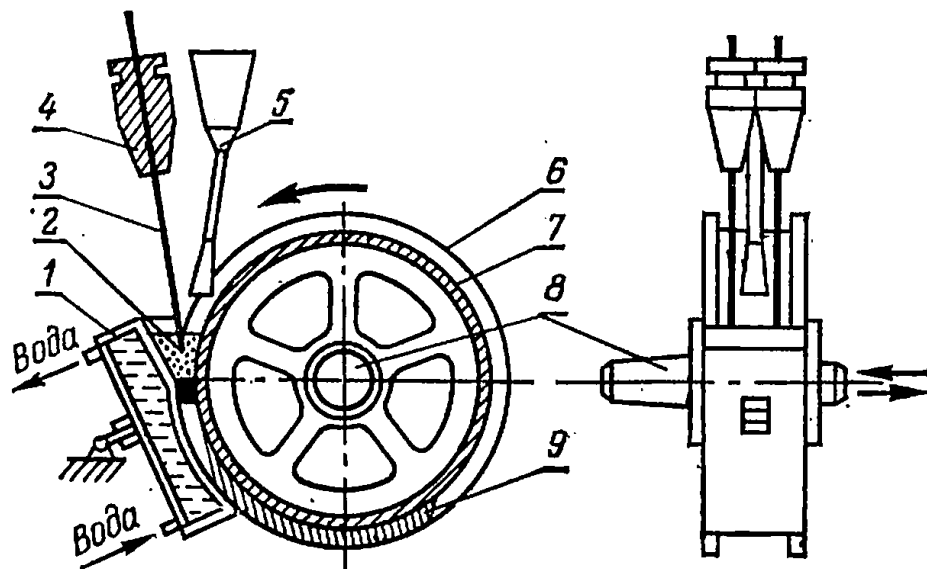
Схема электрошлаковой наплавки опорных катков.
